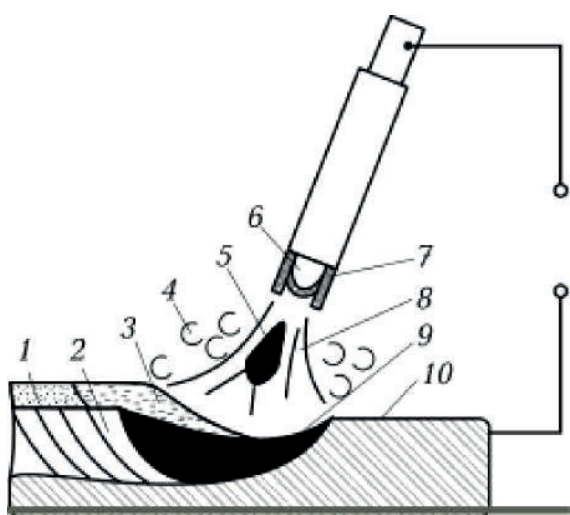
Схема ручного дугового зварювання покритим електродом; 1 – шлакова кірка; 2 – зварний шов; 3 – рідка шлакова плівка; 4 – газовий захист; 5 – крапля електродного металу; 6 – електрод; 7 – електродне покриття; 3 – зварювальна дуга; 3 – зварювальна ванна; 10 – основний метал зварюваної деталі
